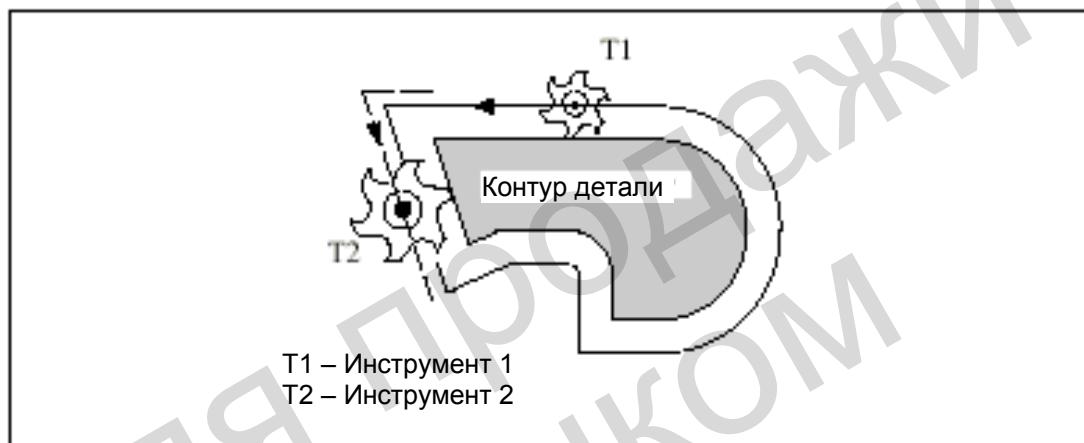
Обработка детали инструментами с различными радиусами
